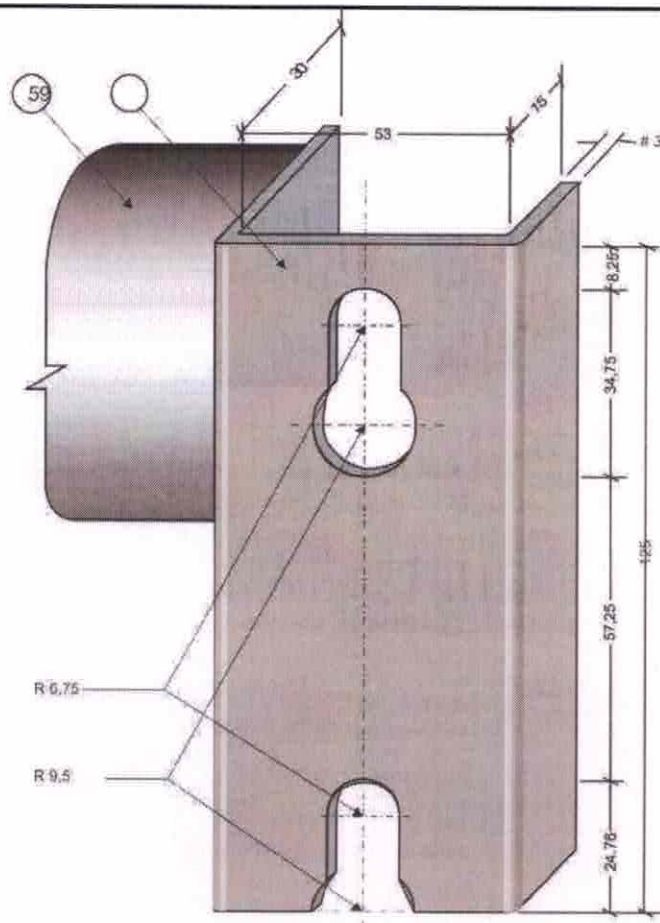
Dispositivo de encaixe fixado nas longarinas (medidas em milímetros)
